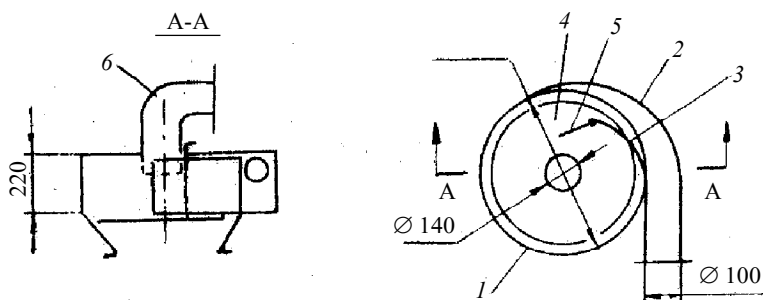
Центробежный разделитель: 1 – корпус, 2 – пневмотранспортный ввод гранулята, 3 – направляющая пластина, 4 – диск формирования вынужденного вихря, 5 – регулирующая шторка, 6 – патрубок вывода воздуха с примесью
